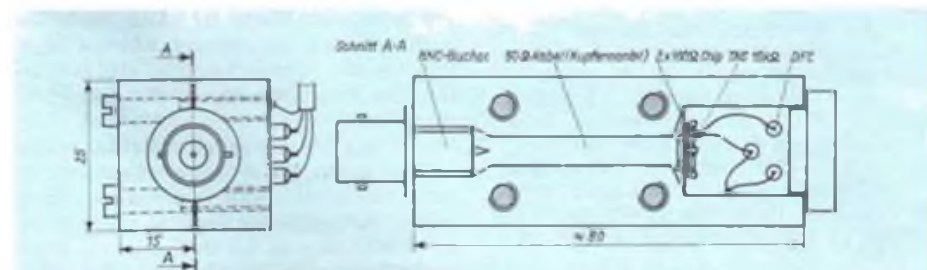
Skizze des mechanischen Aufbaus eines Bolometers
